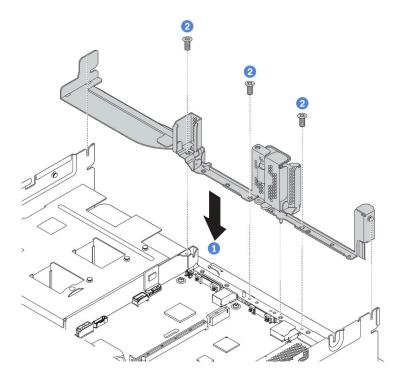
Installazione della staffa posteriore per il montaggio a parete del telaio unità posteriore da 2,5"
